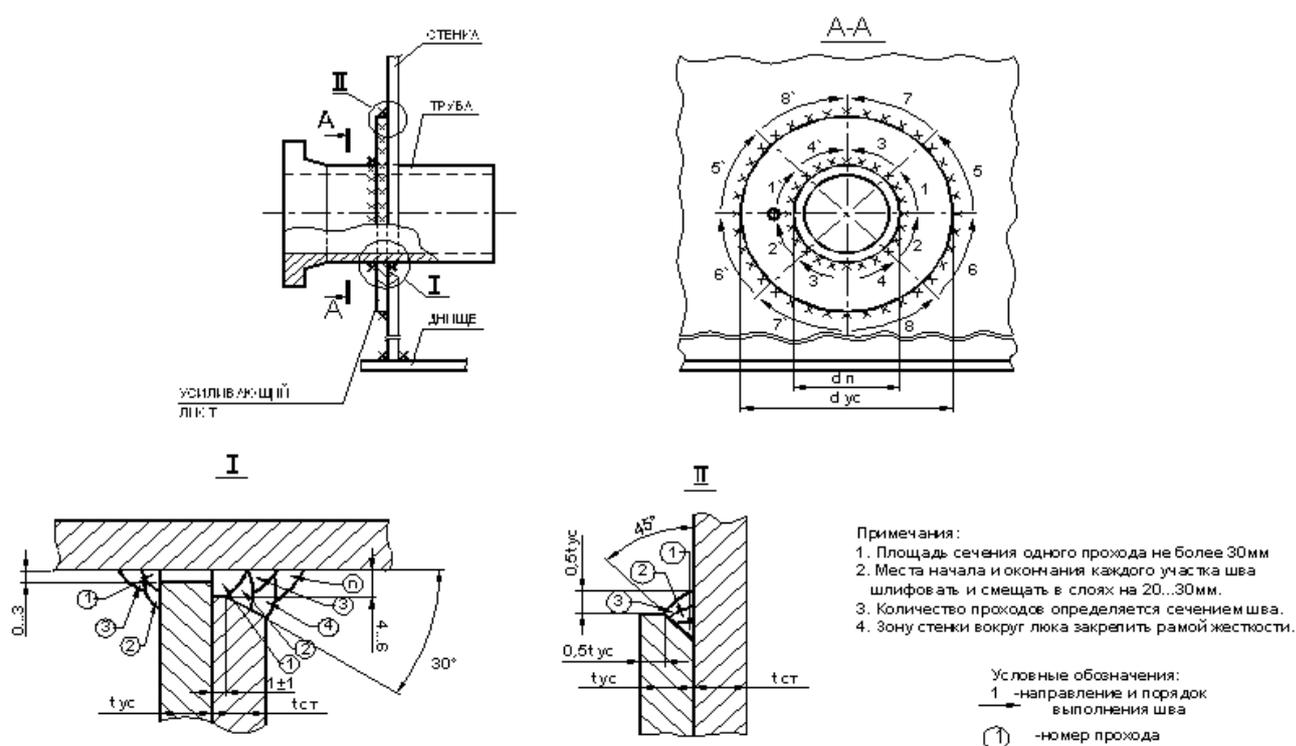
Схема сварки патрубков в стенке с усиливающим листом
